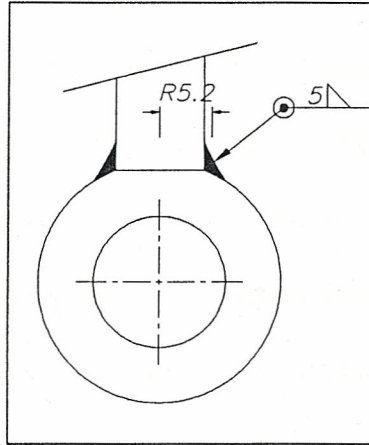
Esquema de las dimensiones de la soldadura en el perno ajustador.
